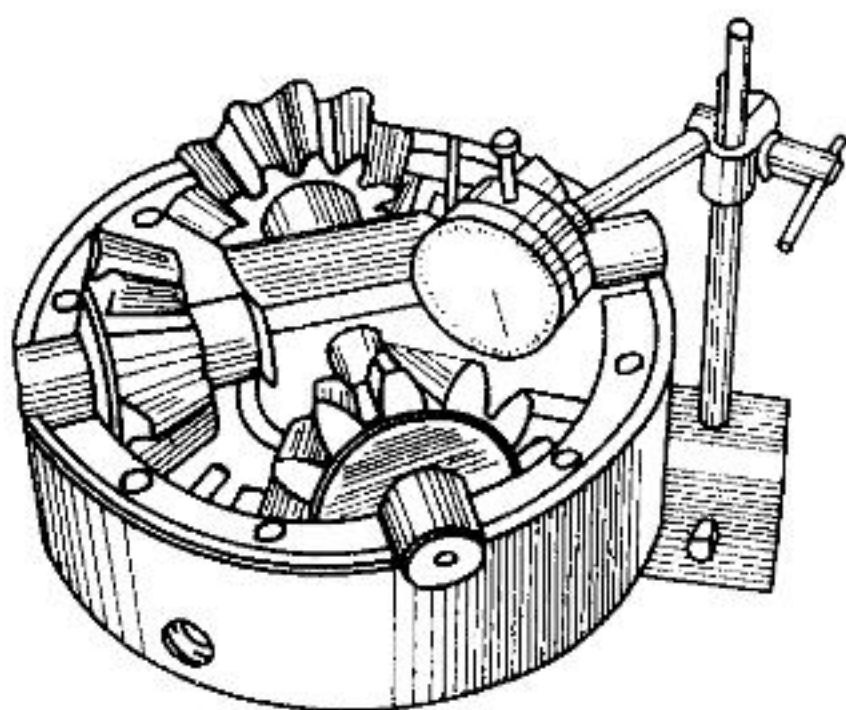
行星齿轮与半轴齿轮啮合间隙的检查
